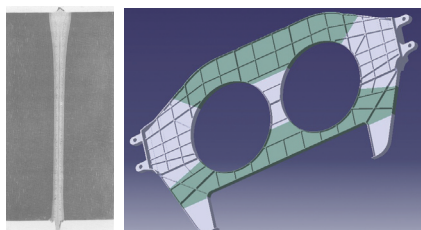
电子束深穿透焊接与飞机钛合金电子束焊接承力结构
